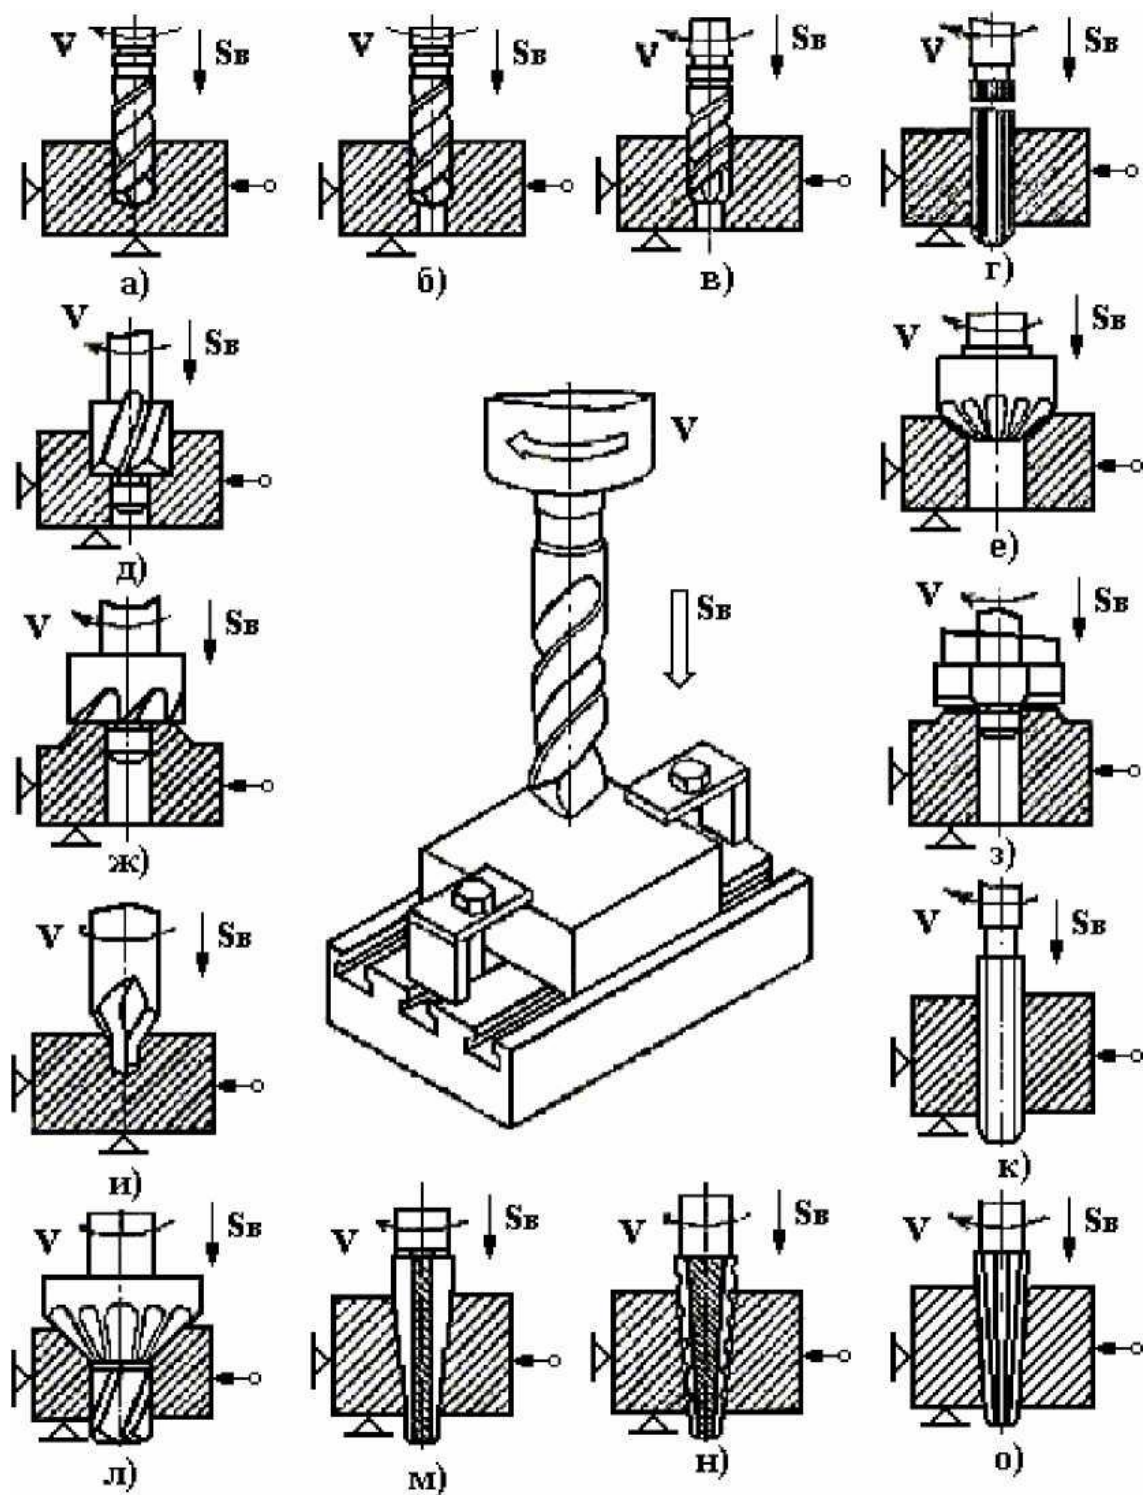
Схемы обработки поверхностей на сверлильных станках: а - сверление; б - рассверливание; в - зенкерование; г - развертывание; д - цилиндрический зенкер (зенковка); е - конический зенкер (зенковка); ж - цековка; з - пластинчатый резец; и - центровочное сверло; к - метчик; л - комбинированный инструмент; м - конический зенкер; н, о- конические развертки
